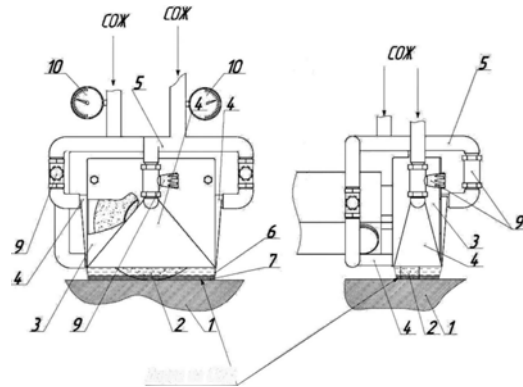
Устройство для комбинаторного способа подачи СОЖ
